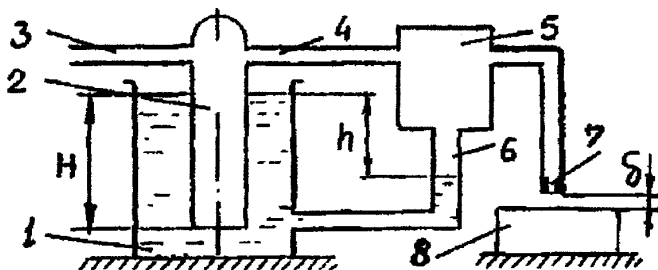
Схема пневматичного вимірювального приладу ("Солекс"): 1 - балон; 2 - труба; 3 - трубка; 4 - вхідна труба камери; 5 - камера; 6 - скляна трубка; 7 - вимірювальний отвір; 8 - деталь
